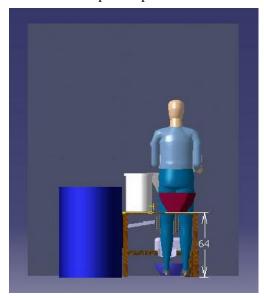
Desain Stasiun Penggilingan Tampak Samping Kanan lama
